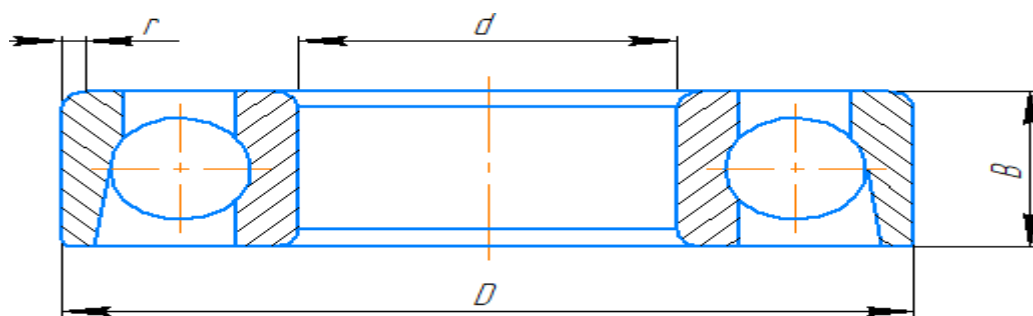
Эскиз радиально-упорного однорядного подшипника (ГОСТ 831-775)
